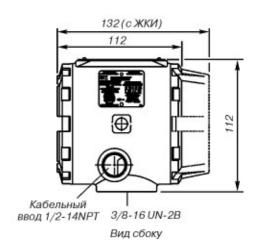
Габаритный чертеж преобразователя. Кабельный ввод 1/4-NPT\*.
